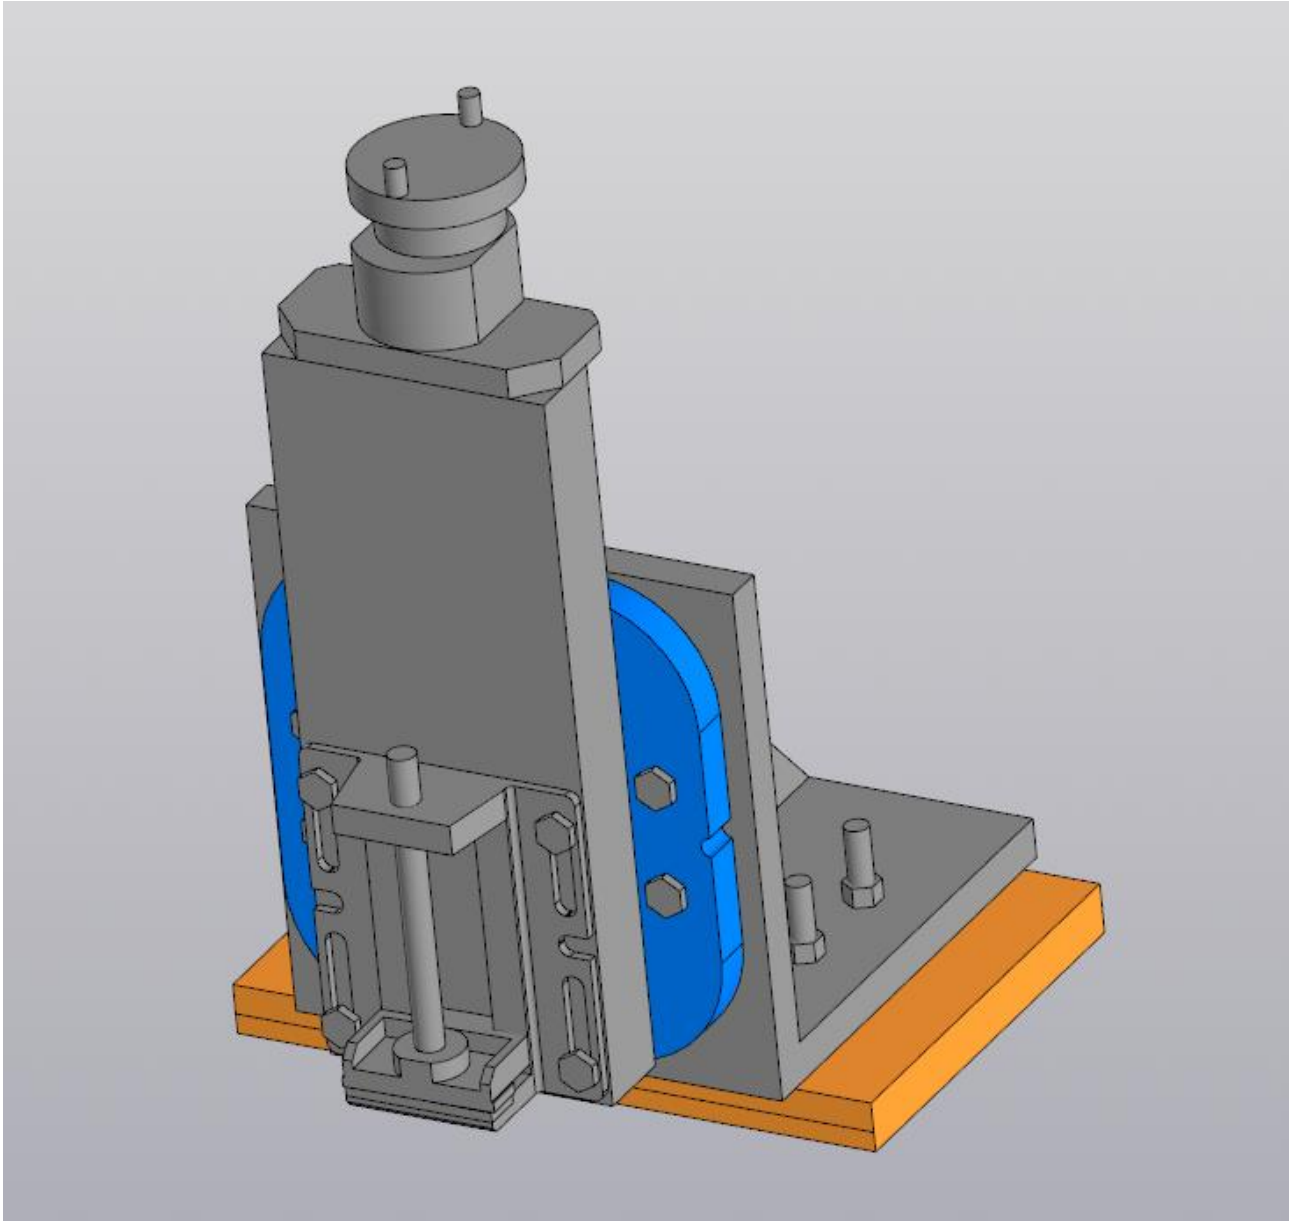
Модель пристрою для виконання фрезерних операцій на токарно-гвинторізальному верстаті 16К20
